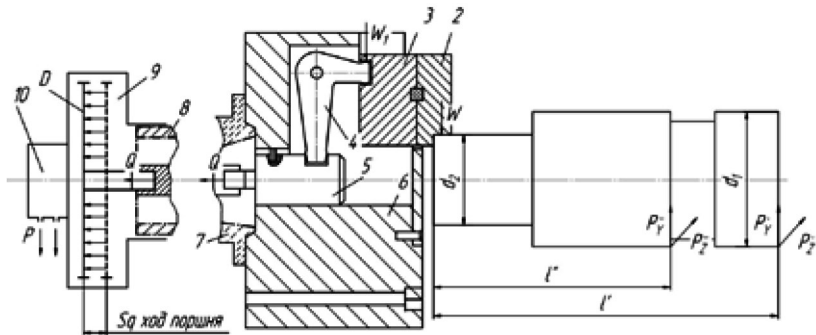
Схема закрепления заготовки в трёхкулачковом самоцентрирующем патроне: 1 – заготовка; 2 – кулачок сменный; 3 – кулачок постоянный; 4 – зажимной механизм (рычажной); 5 – втулка центральная; 6 – корпус; 7 – передняя часть шпинделя; 8 – задняя часть шпинделя; 9 – вращающаяся ось силового привода; 10 – муфта для подвода рабочей среды
